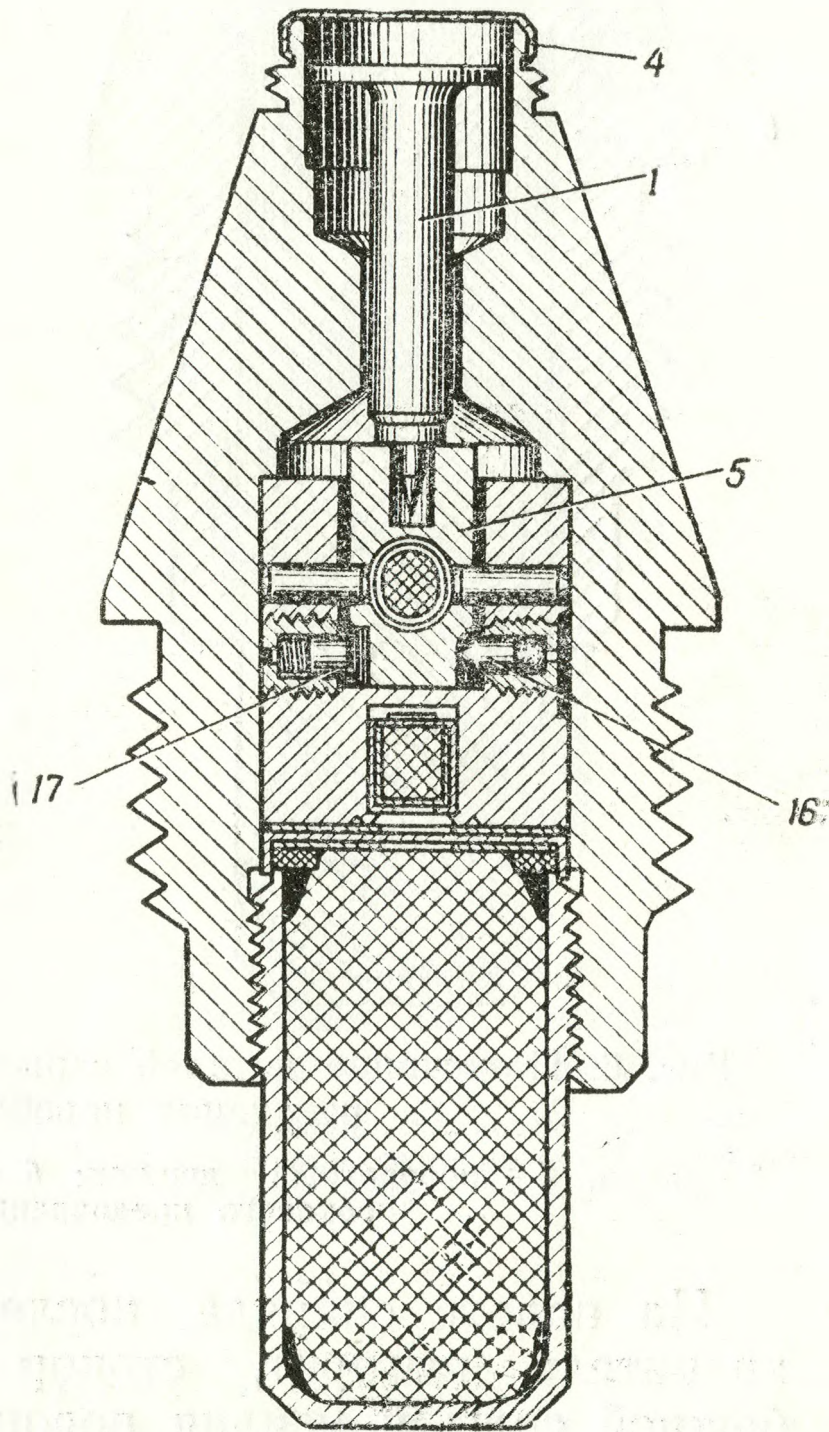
Положение деталей взрывателя при вылете снаряда из канала ствола орудия: 1 — ударный стержень; 4 — мембрана; 5 — поворотный движок; 16 — стопор; 17 — стопор
